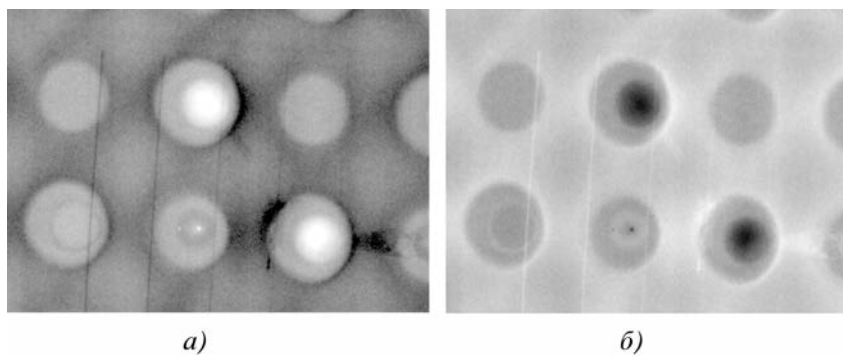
Цифровые изображения дефектного участка образца с двойной точечной сваркой, полученные с применением твердотельного преобразователя: а – негатив; б – позитив
